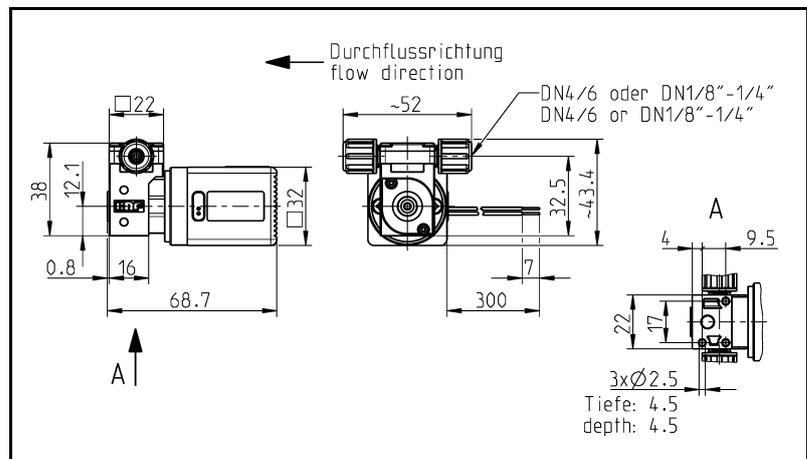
Befestigungsmasse NF 1.25 DCB-B
